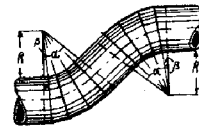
Сварная утка, состоящая из шести звеньев и четырех стаканов.
